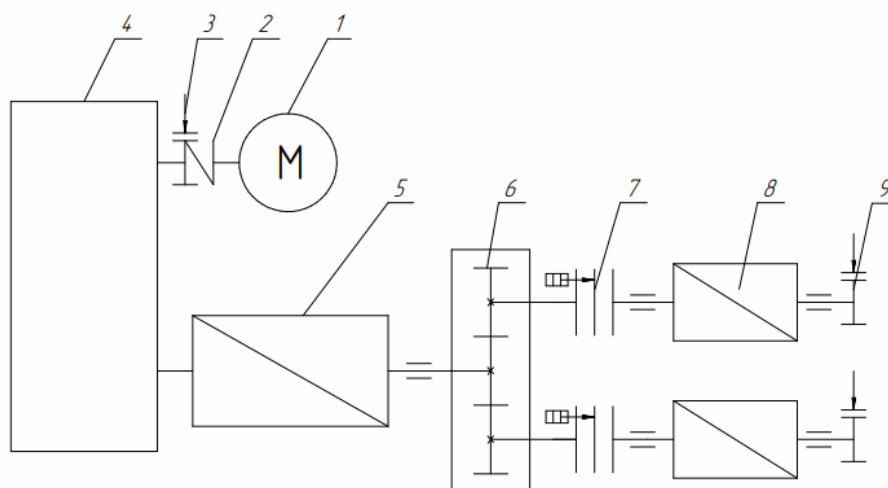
Кинематическая схема модернизированного привода механизма подъёма: 1 – электродвигатель, 2 – упругая муфта, 3 – тормоз, 4 – цилиндрический редуктор, 5 – грузовой барабан, 6 – зубчатая передача, 7 – гидростатическая муфта, 8 – барабан подвижного противовеса, 9 – тормоз
